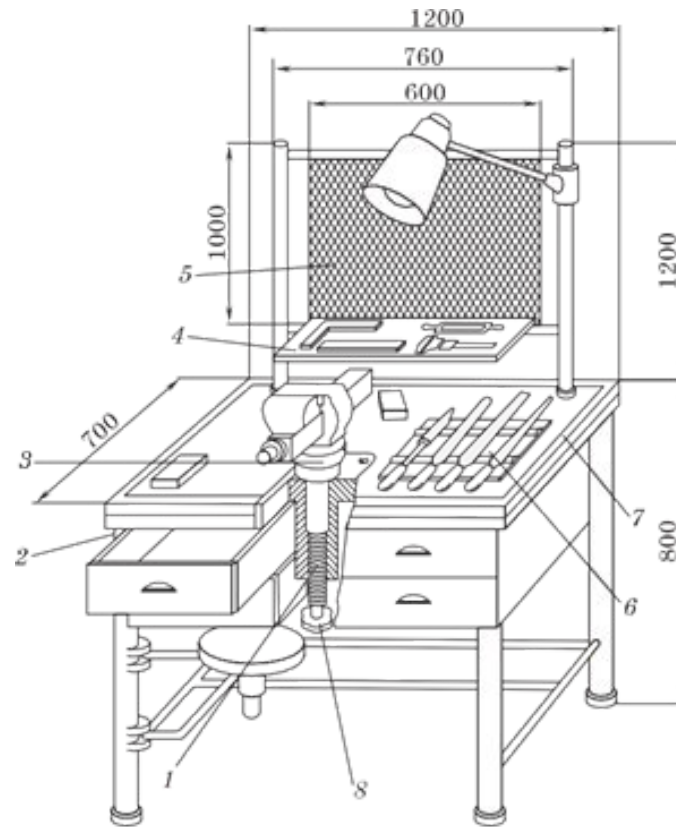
Слесарный верстак с регулируемым по высоте тисками: 1 — регулирующий винт; 2 — каркас; 3 — хвостовик тисков; 4 — полочка для измерительного инструмента; 5 — защитный экран; 6 — планшет для рабочего инструмента; 7 — планки-бортики; 8 — маховичок
